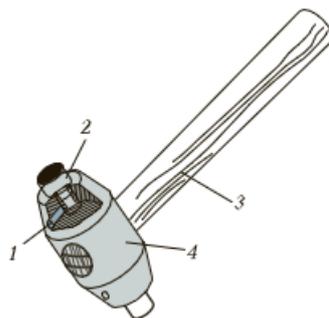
Молоток с мягкой вставкой: 1 — штифт; 2 — боек; 3 — рукоятка; 4 — корпус
